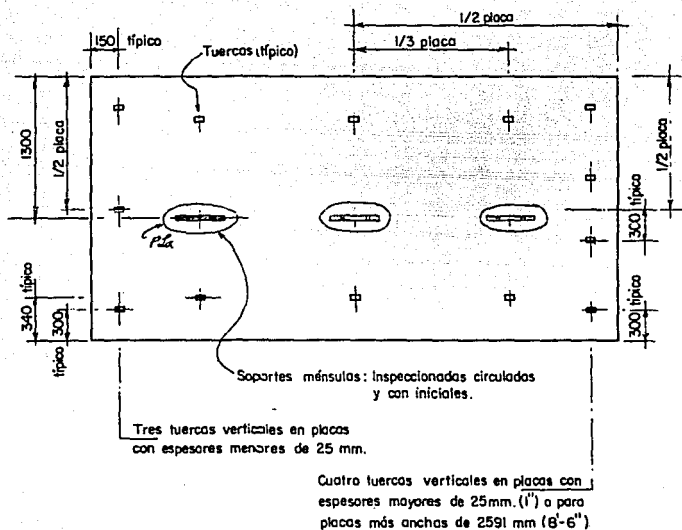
LOCALIZACION DE TUERCAS Y MENSULAS PARA SOLDARLAS ANTES DEL MONTAJE.
